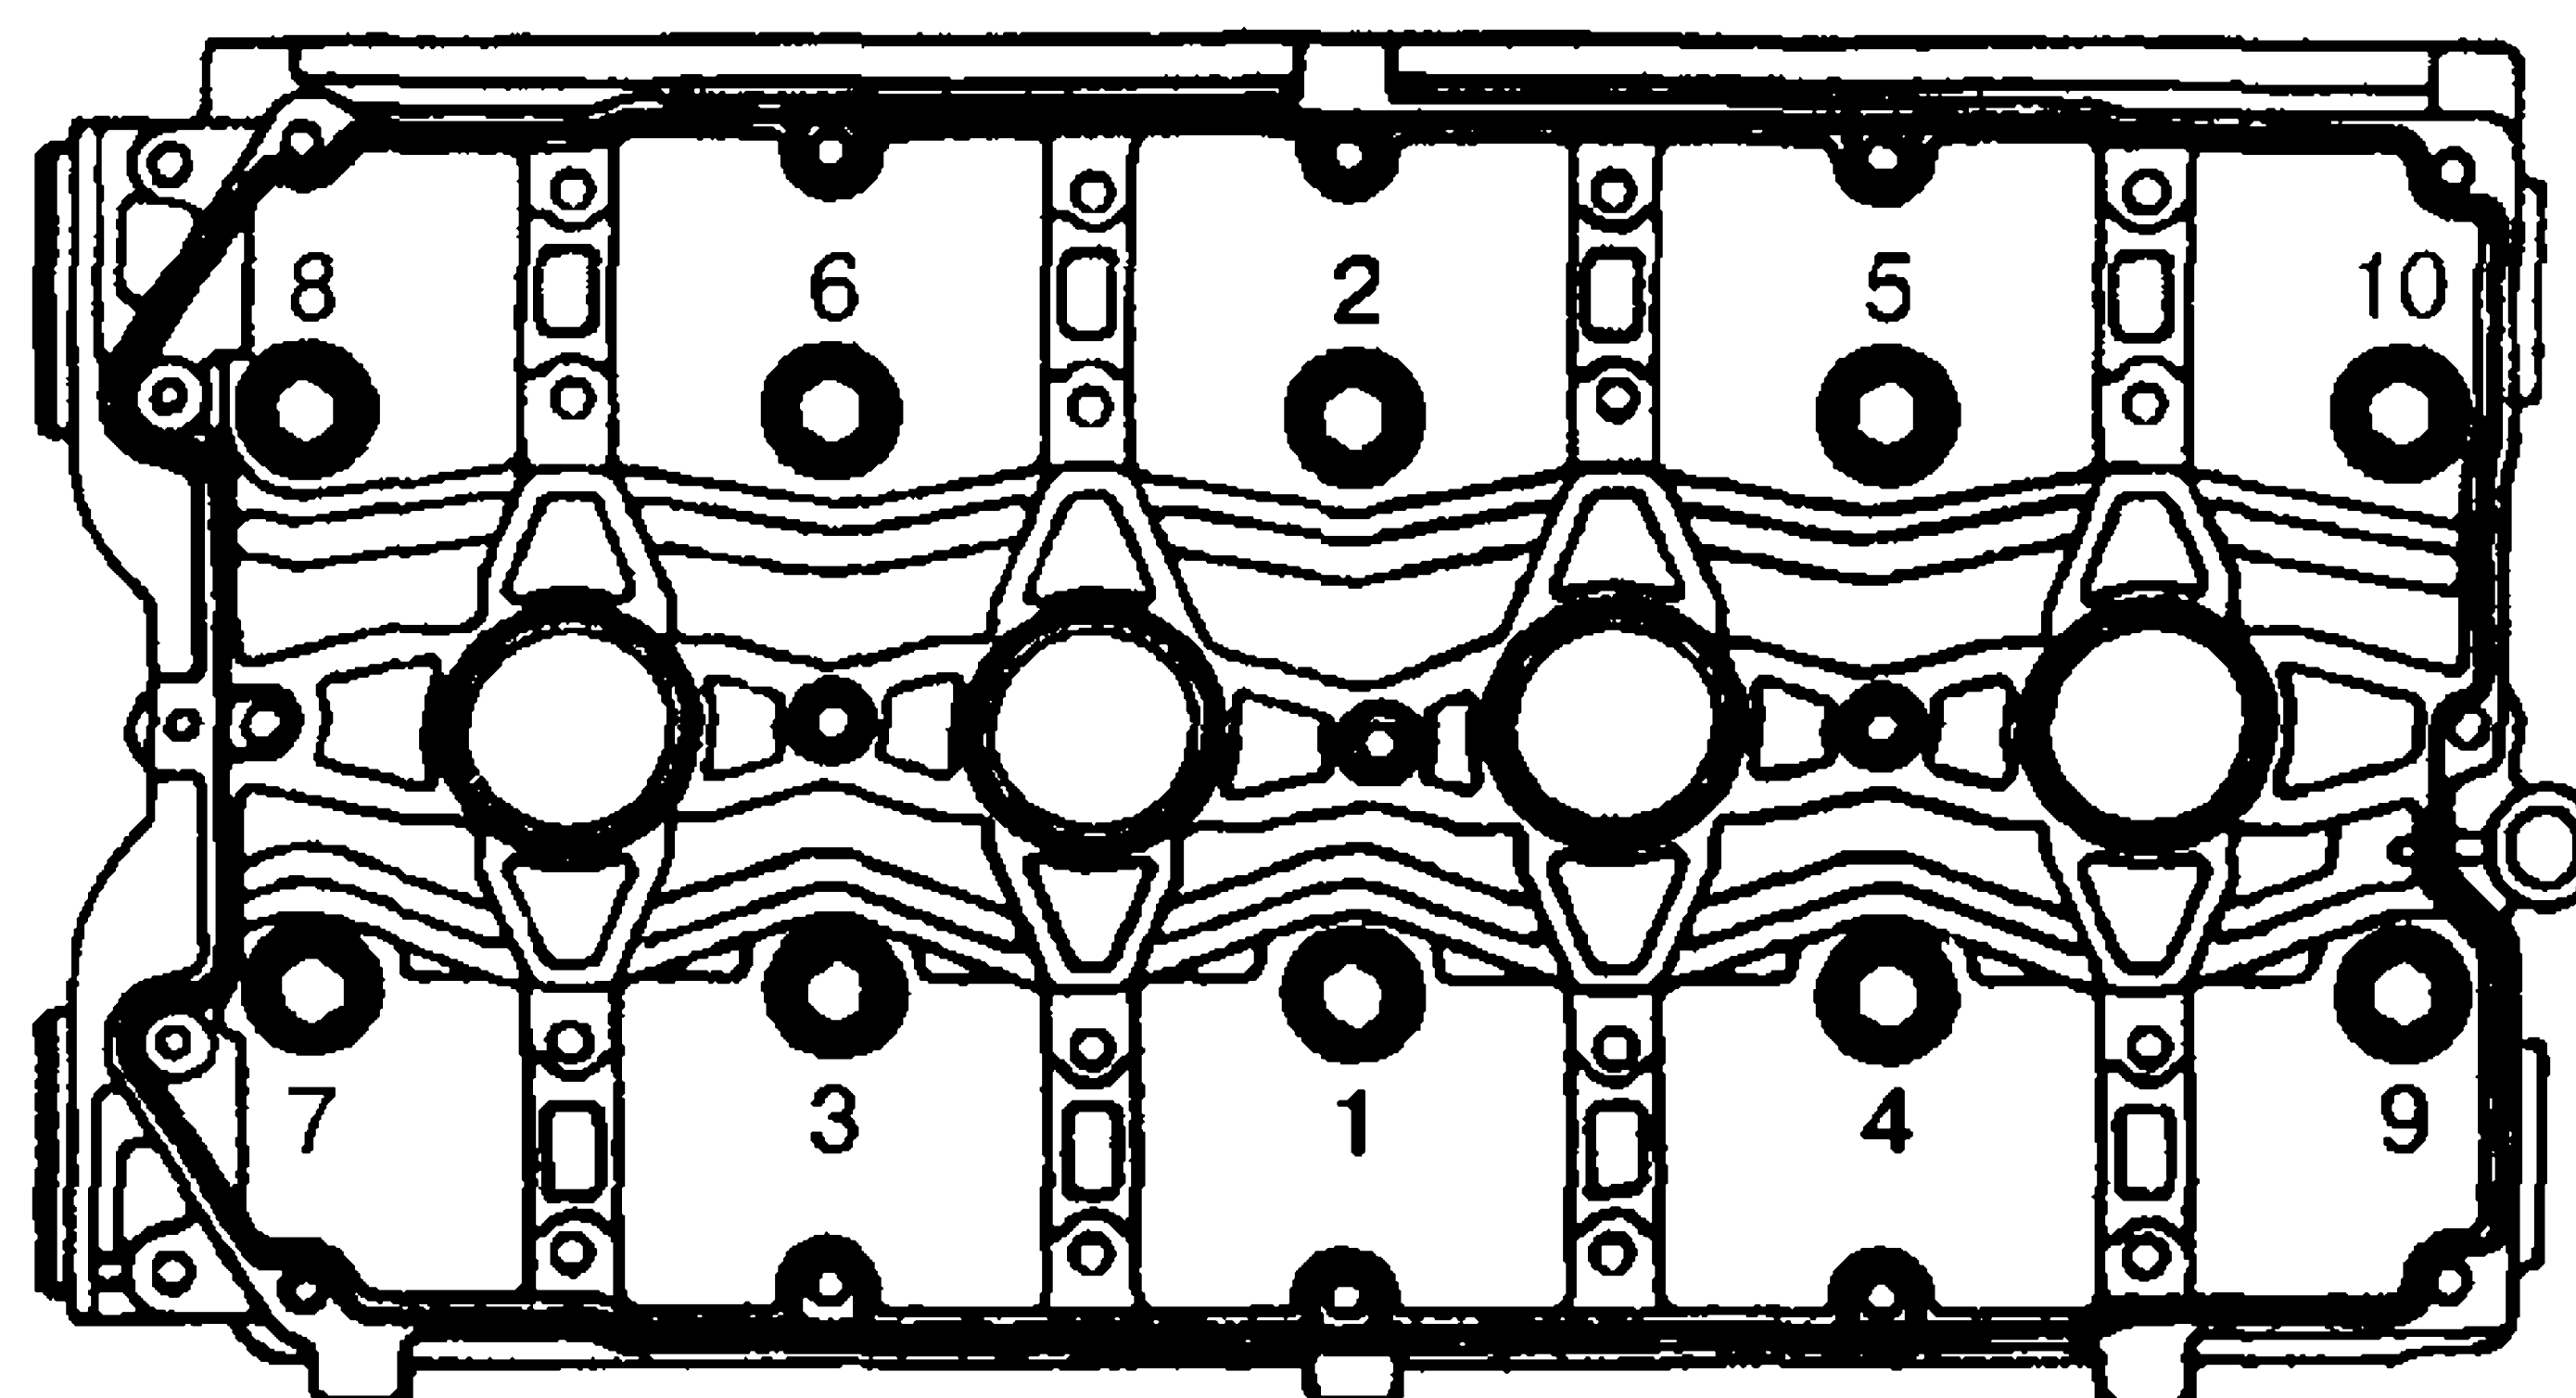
Порядок затяжки болтов крепления головки цилиндров и схема нанесения герметика на корпус подшипников распределительных валов
